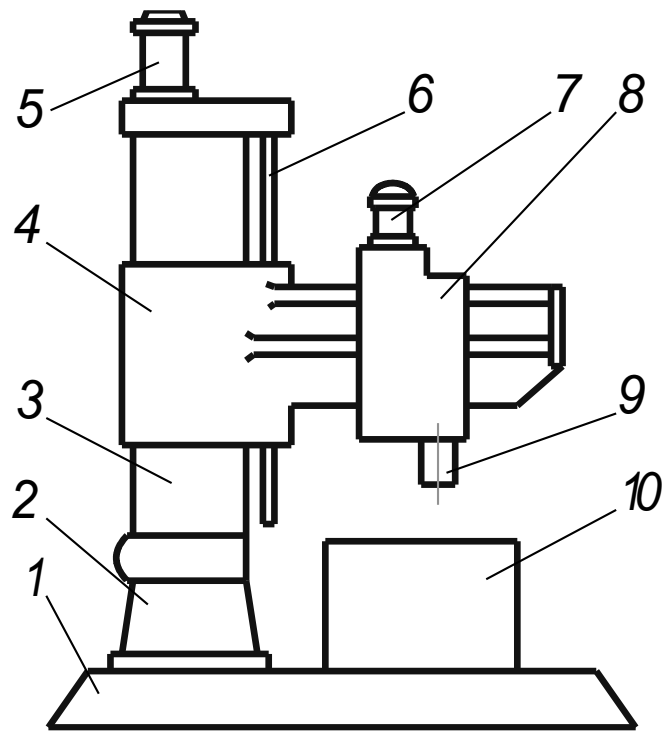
Загальний вигляд радіально-свердлильного верстата
